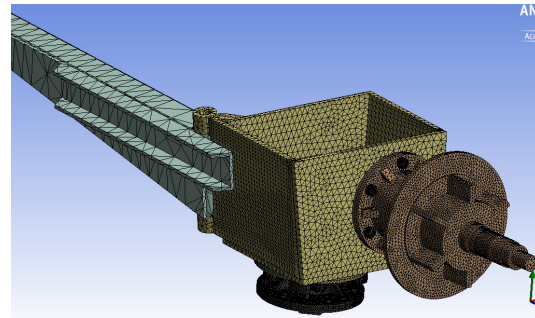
Malla del ensamble superior desde vista frontal izquierda.
